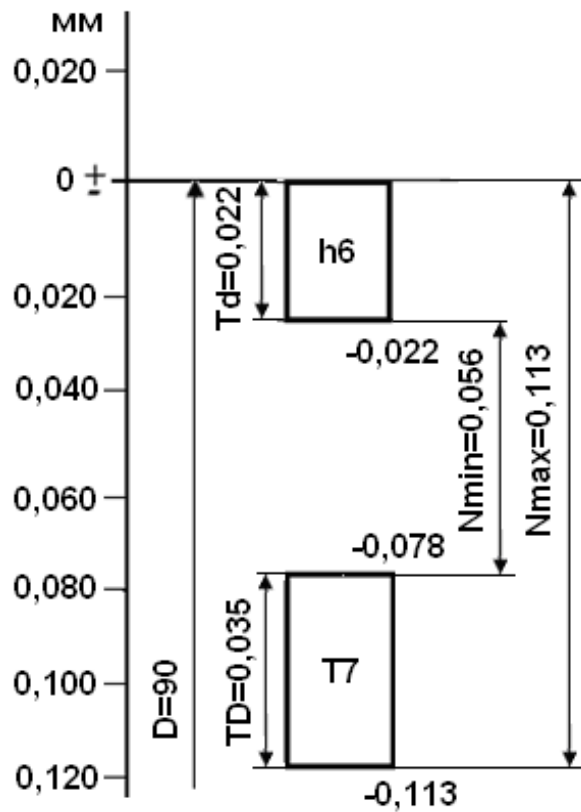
Схема розташування полів допусків деталей з'єднання  $\varnothing 90T7/h6$
